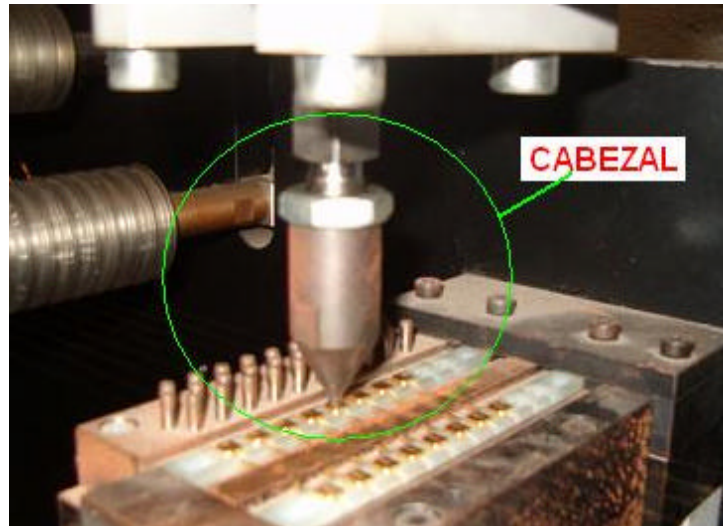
Cabezal de estampado de la máquina de hilos
